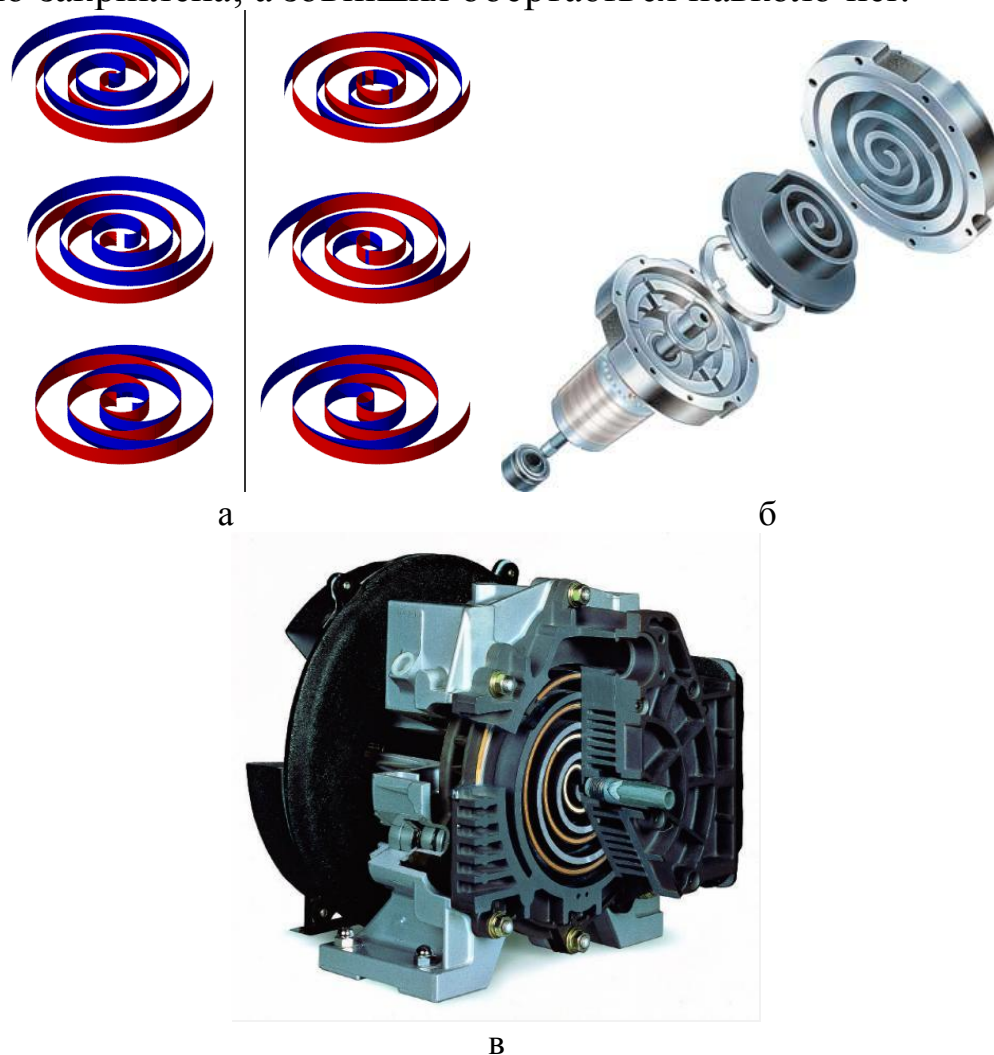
Спіральний компресор: а – схема роботи спірального компресору; б – конструкція робочого органу; в - зовнішній вигляд у розрізі спірального компресору
